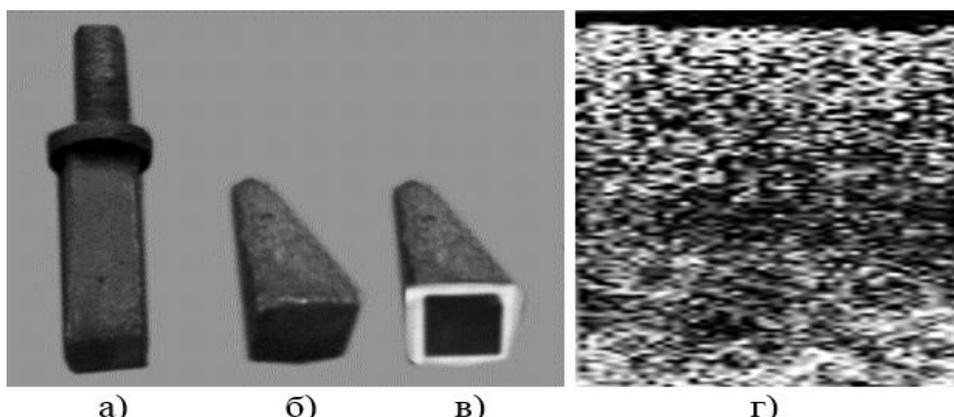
Стальная отливка детали и вырезанные образцы с твердосплавным покрытием: а-отливка детали; б-вырезанные куски образца детали в шлифованном и полированном виде; в-травленный образец с толщиной покрытия 2,5 мм; г-структура поверхностного покрытия толщиной слоя 3,0 мм. X500
